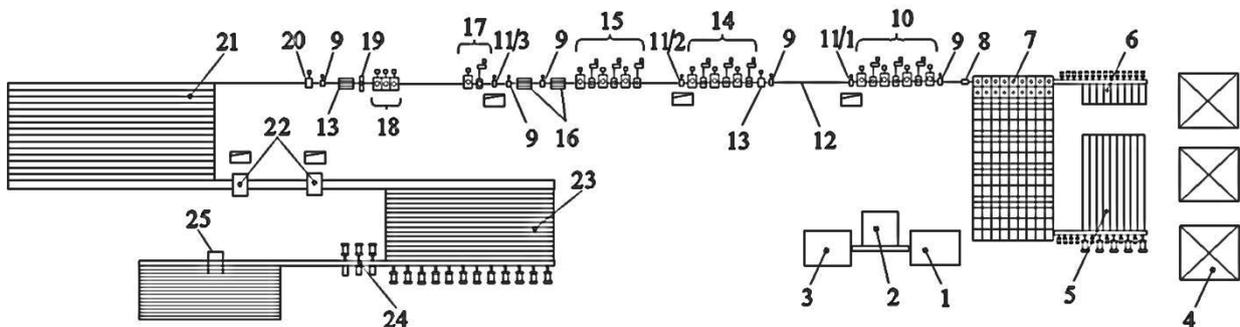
Упрощенная схема прокатного стана 370/150 при производстве сортового проката в прутках: 1 – дробеструйная установка; 2 – магнитолуминесцентный метод определения дефектов; 3 – шлифовальный станок; 4 – склад заготовок; 5 – загрузочная решетка; 6 – аварийная решетка; 7 – нагревательная печь; 8 – устройство гидросбива окалины; 9 – трайб-аппарат; 10 – 1–7 клетки черновой группы; 11 – зачистные ножицы; 12 – терморольганг; 13 – обрывные ножицы; 14 – 8–13 клетки первой промежуточной группы; 15 – 14–19 клетки второй промежуточной группы; 16 – трасса термоупрочнения; 17 – 20–21 клетки предчистовой группы; 18 – редуциционно-калибровочный блок; 19 – установка измерения диаметра HiGauge; 20 – делительные ножицы; 21 – холодильник; 22 – дисковые пилы; 23 – цепное передающее устройство; 24 – упаковочные машины; 25 – измерительный стенд массы
